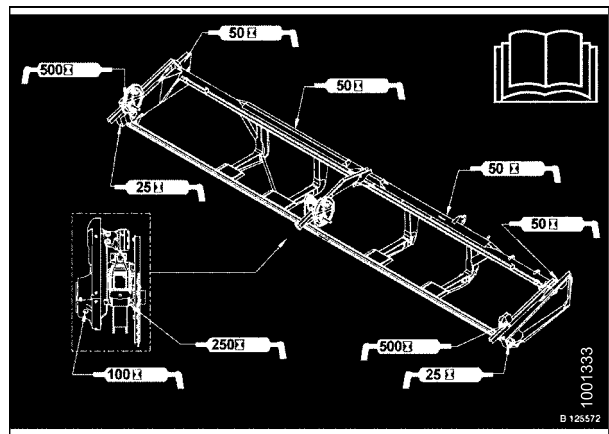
Наклейка с основными точками смазки на жатке с двойным ножом
